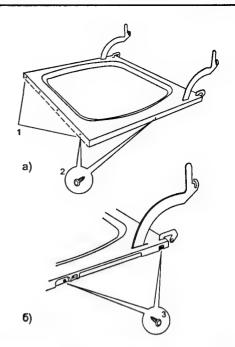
Операции с дверцей корпуса: а — замена ручки и внутренней части дверцы; б — заме-
